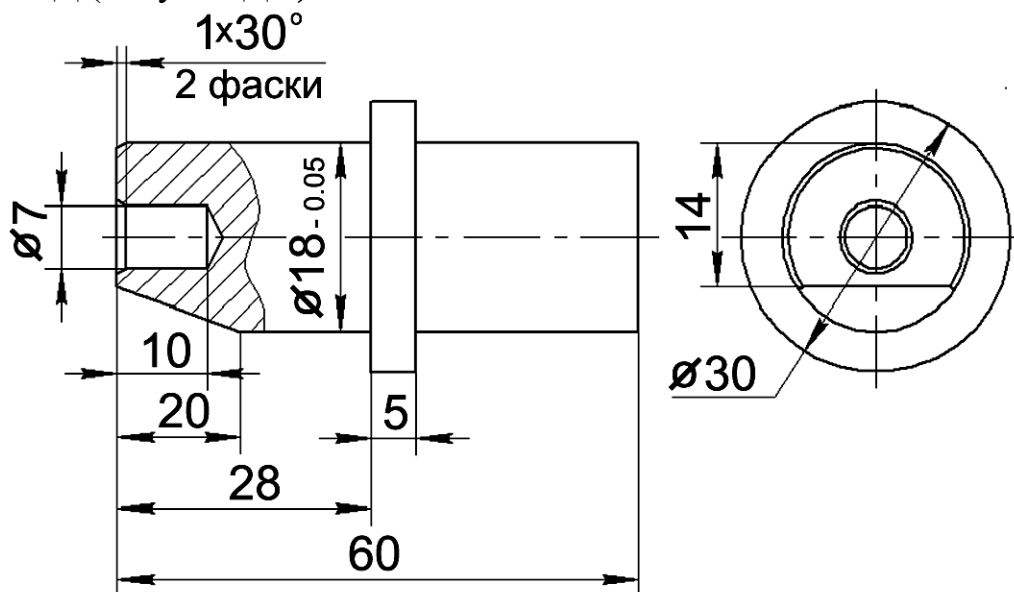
Приспособление для фиксации установочного штифта.
